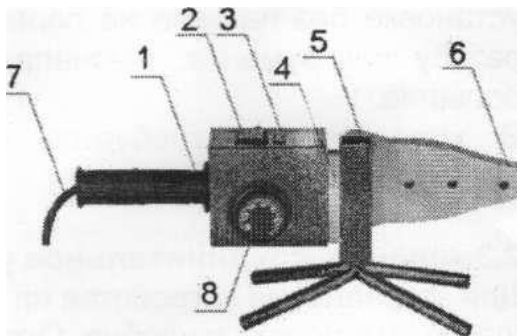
Електрозварювальний апарат для поліфузного зварювання Ритм ППТ-2000: 1- шасі; 2- кнопка включення; 3- індикаторна лампочка; 4- теплоізоляційний кожух; 5- опора; 6- нагрівальна плита; 7- провід; 8- терморегулятор.
